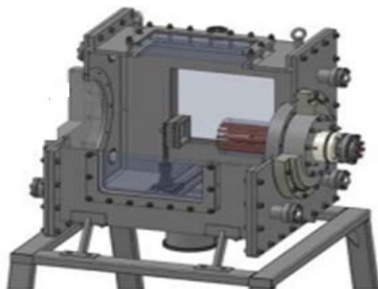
Схема расположения заготовки в вакуумной камере при обработке поверхности с помощью воздействия КПП
